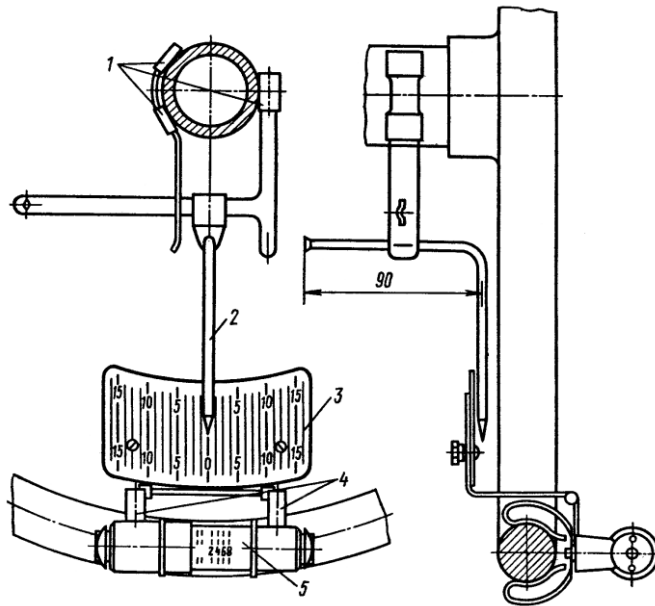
Люфтомер К-187: 1 – захваты рулевой колонки, 2 – указатель, 3 – шкала люфтомера, 4 – зажимы для крепления на рулевом колесе, 5 – динамометрическая рукоятка
